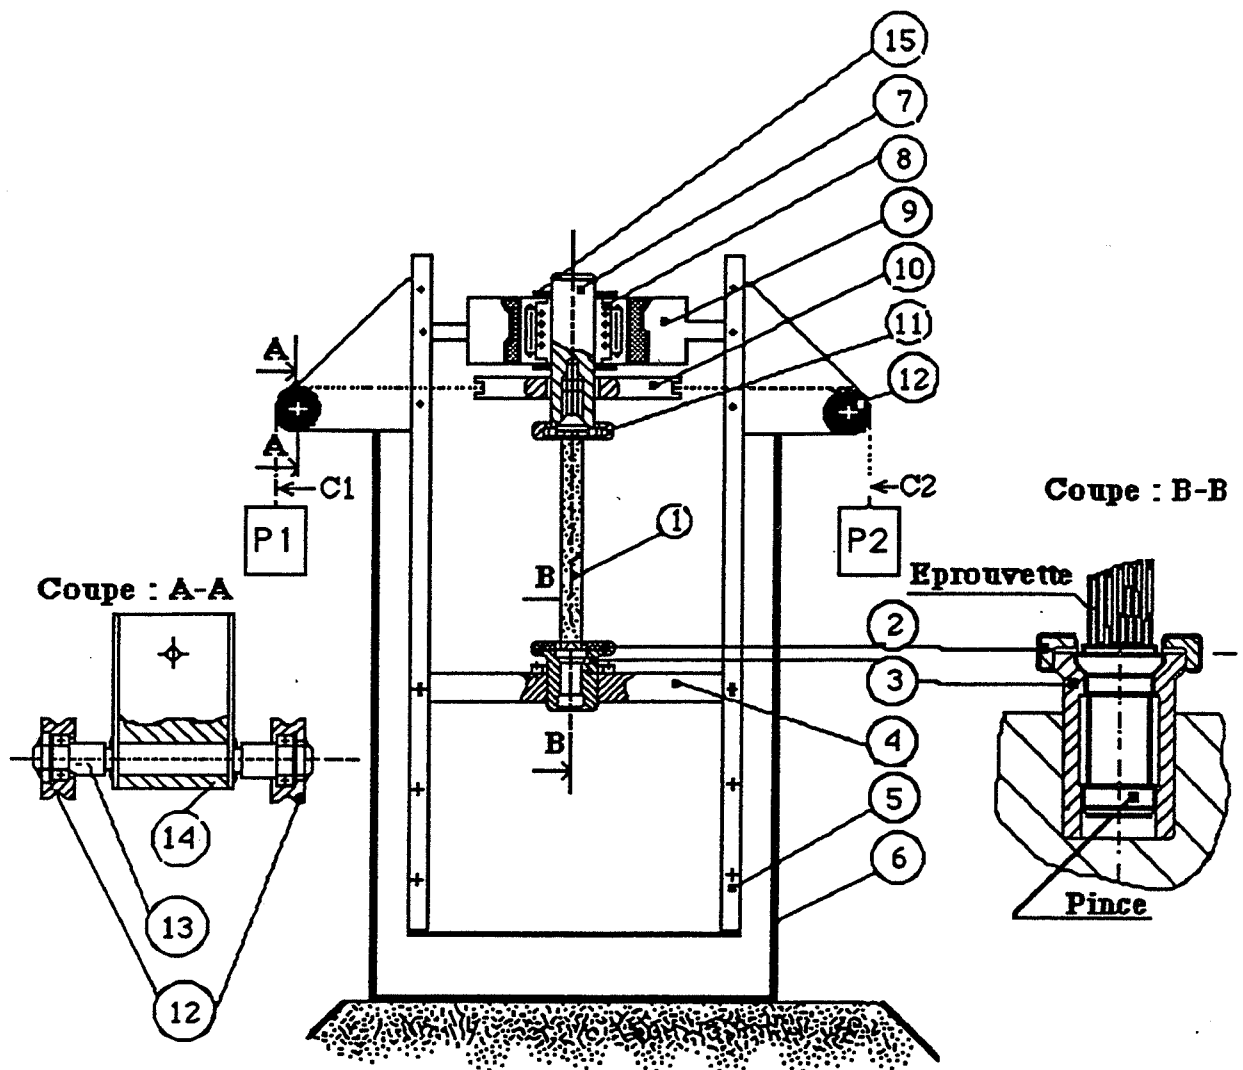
Dessin d'ensemble de la machine de torsion verticale.
